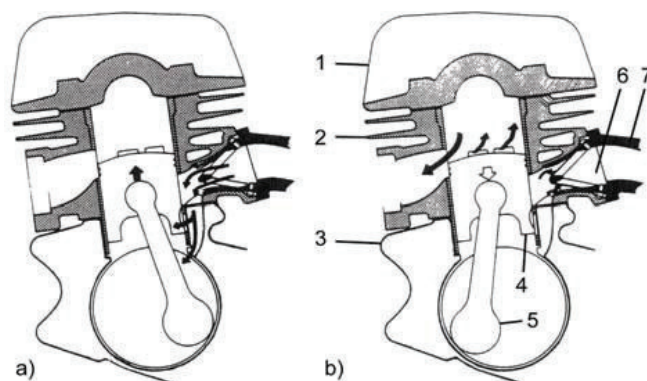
Motor se souproutým vyplachováním pomocí ventilu [5]
